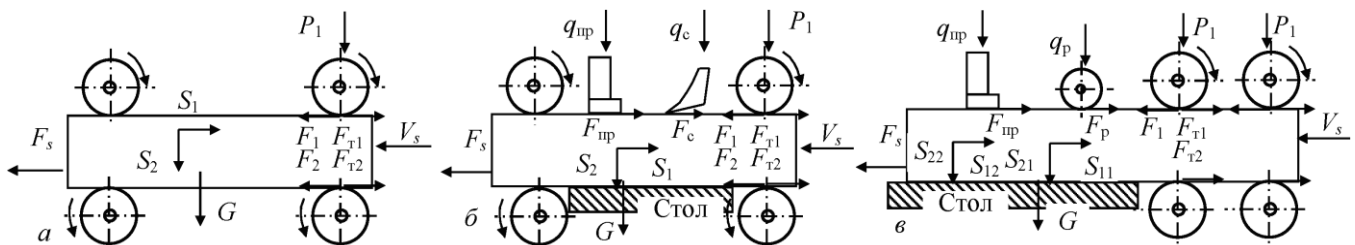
Розрахункові схеми механізмів подачі верстатів: а - круглопилевого; б - рейсмусового; в - багатшпindelного поздовжньо-фрезерного
